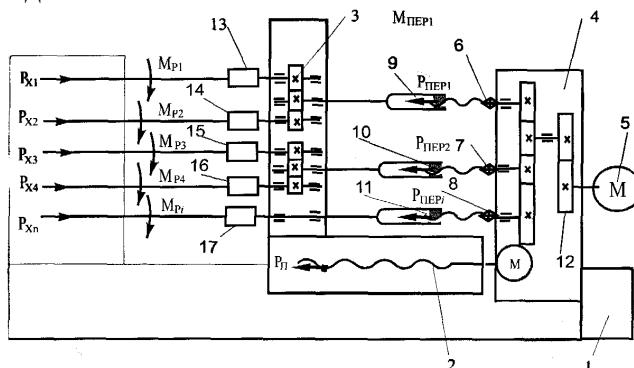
Силова багатошпиндельна головка з механізмом керування пружними деформаціями із загальною ланкою настроювання
